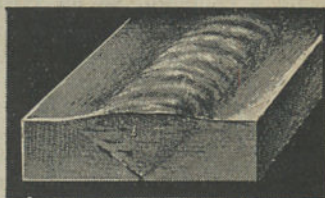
Colagem revelada pelo ensaio de corrosão.
